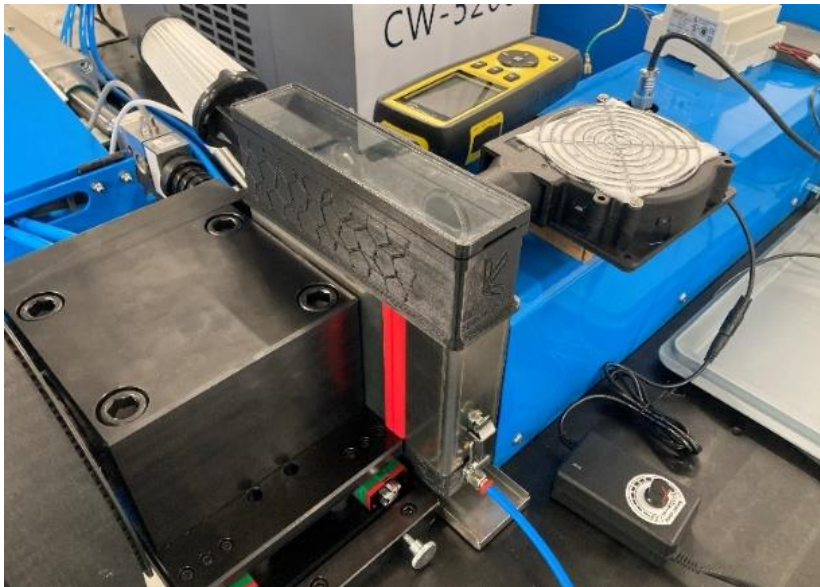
Detail způsobu těsnění plechů. Zdroj: autor.
